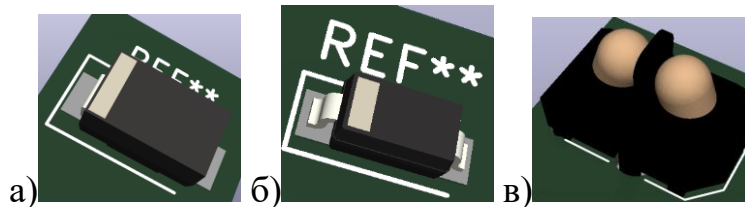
Загальний вигляд корпусів: а) DO-214AC; б) SOD-123; в) TCRT5000
